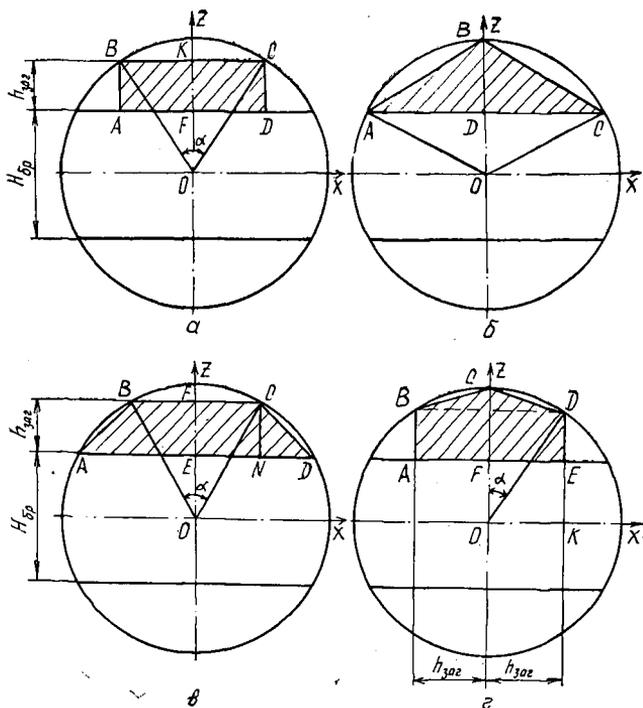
Схема выработки из сегментов пиломатериалов различного сечений: а — прямоугольное; б — треугольное; в — трапецидальное; г — пятигранное
